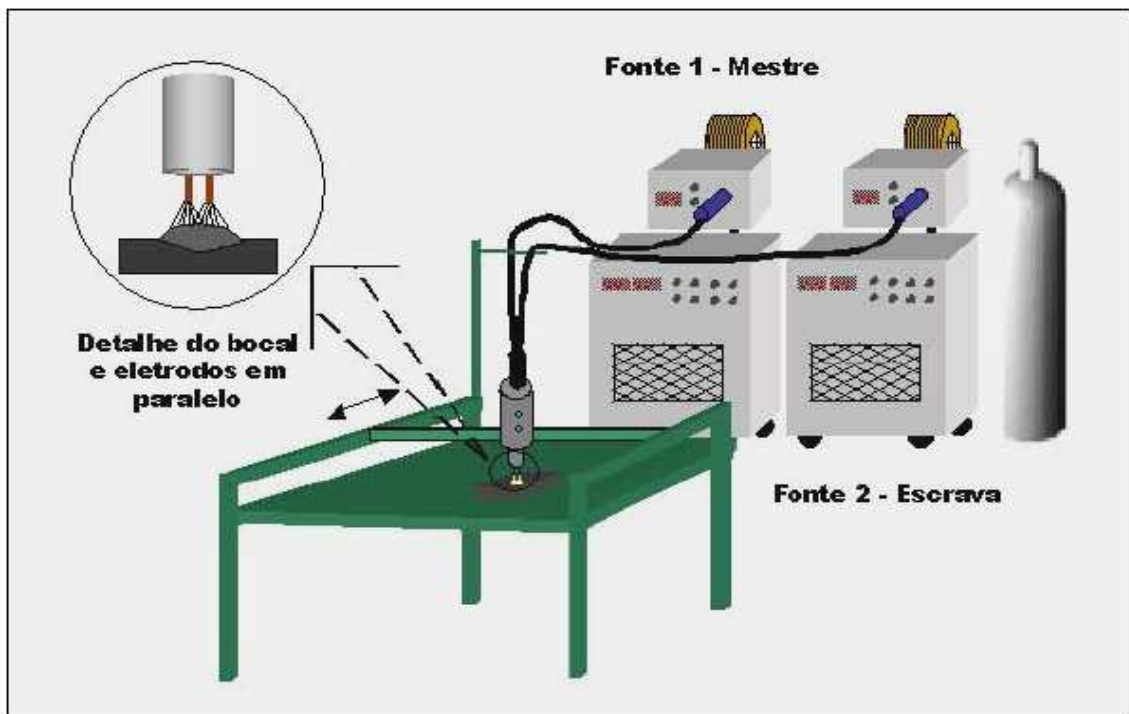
Esquema da soldadura MIG/MAG de arame duplo [Groet 2005]
